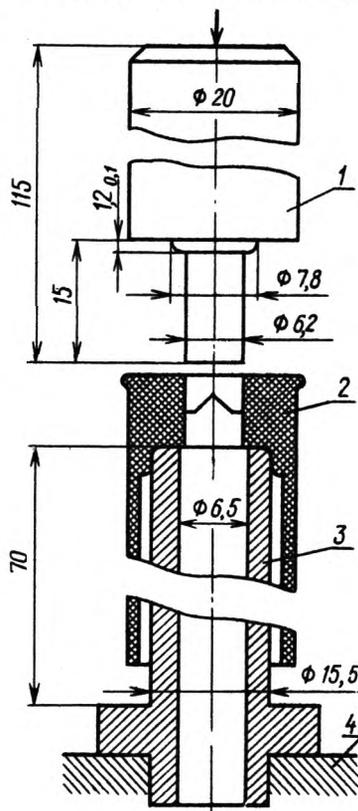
Приспособление для обработки капсюльных гнезд под капсюль Жевело: 1 — пуансон; 2 — бумажная гильза; 3 — оправка-матрица; 4 — слесарные тиски.
